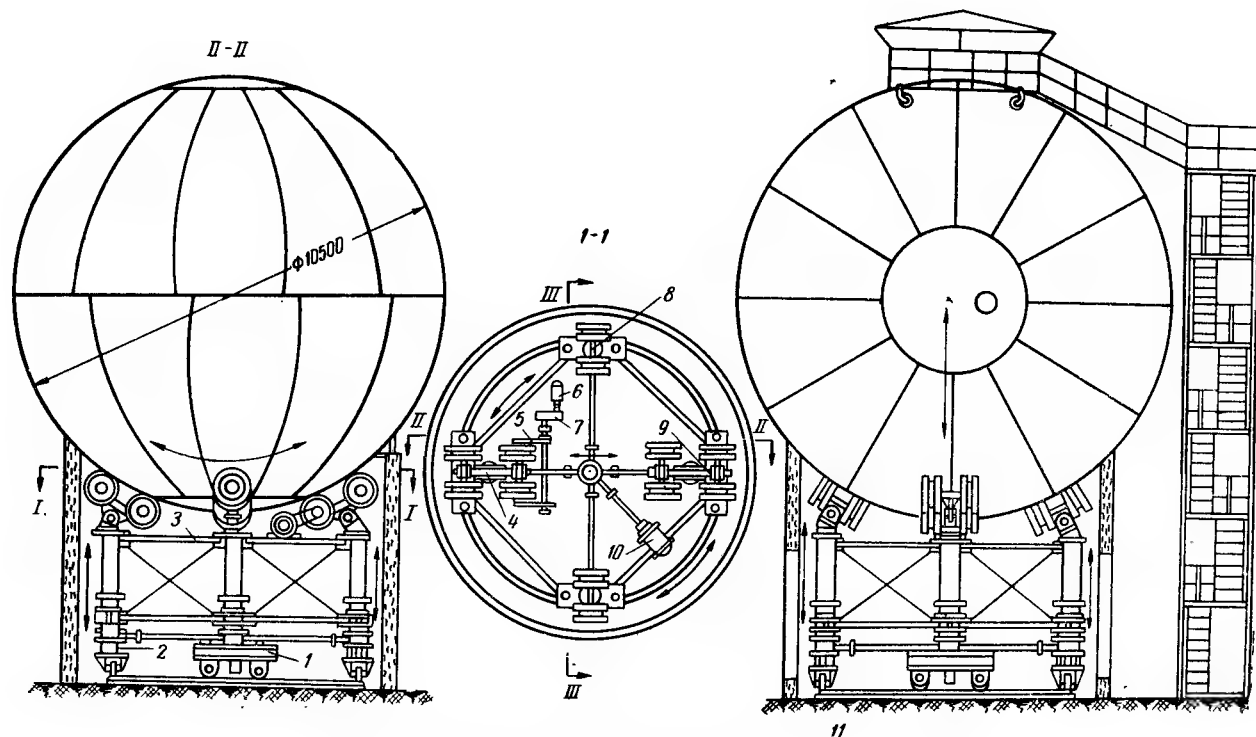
Манipулятор для сварки шаровых резервуаров
